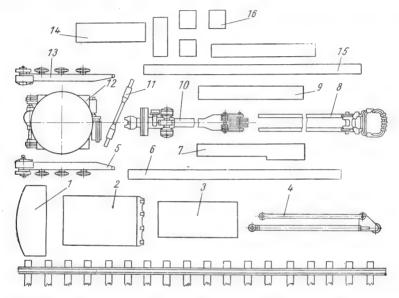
Схема расположения узлов экскаватора на монтажной площадке
